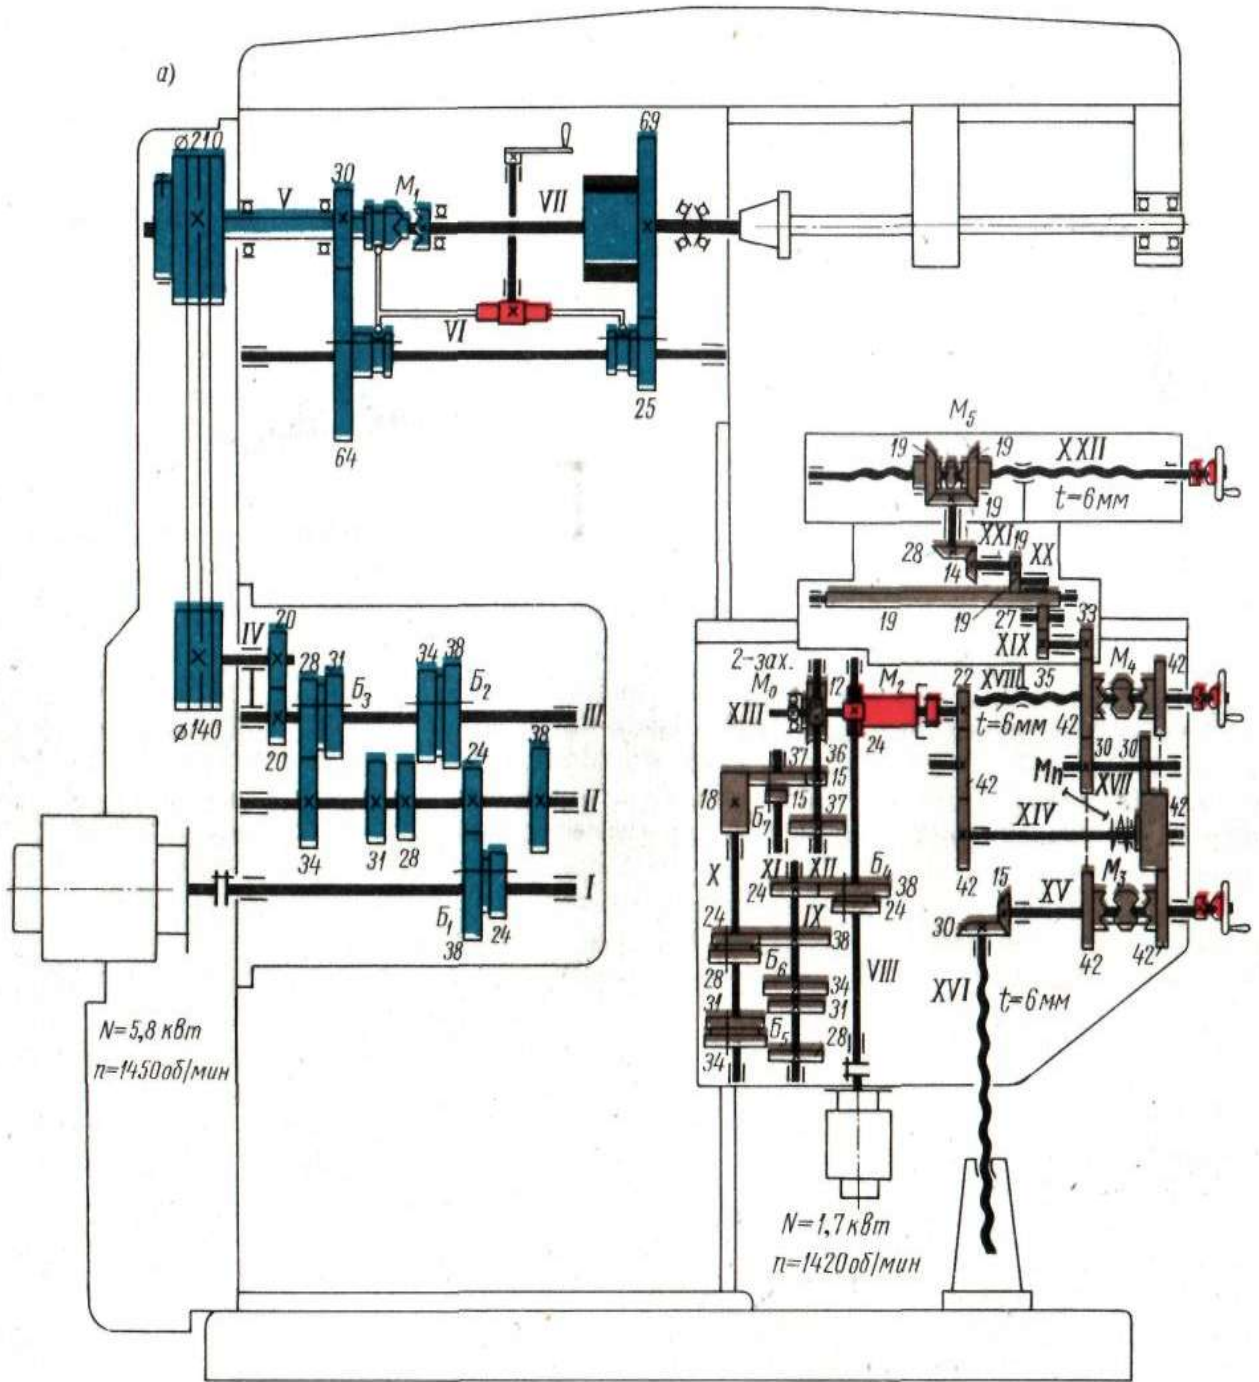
Кинематическая схема универсально-фрезерного станка модели 6Н81
